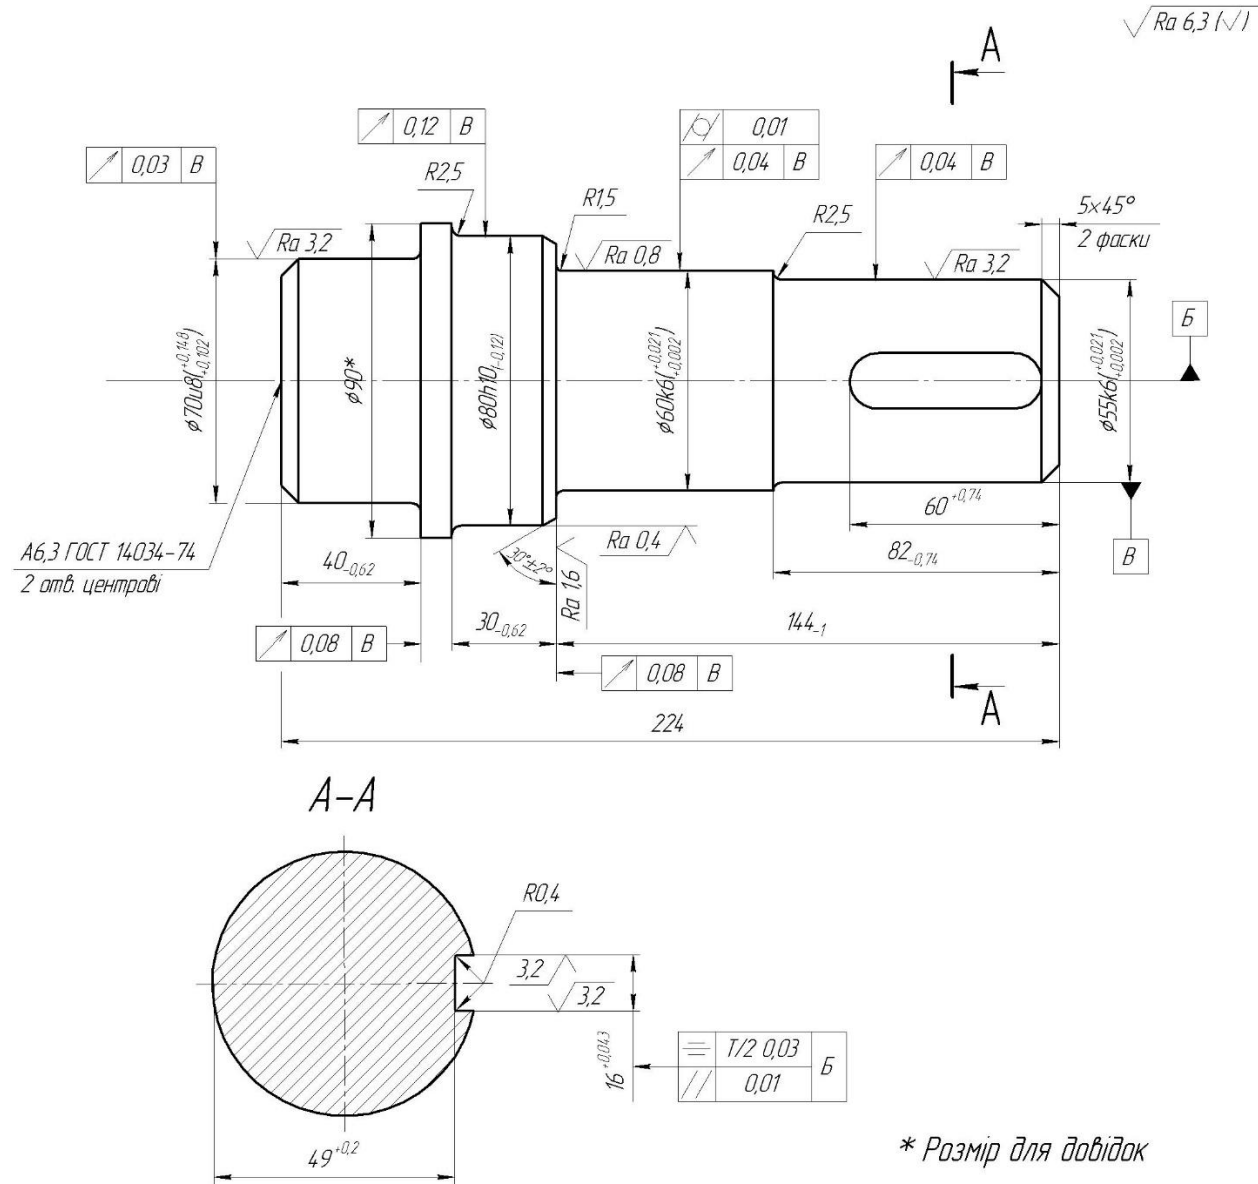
Кресленик деталі «Вал ступінчастий»
